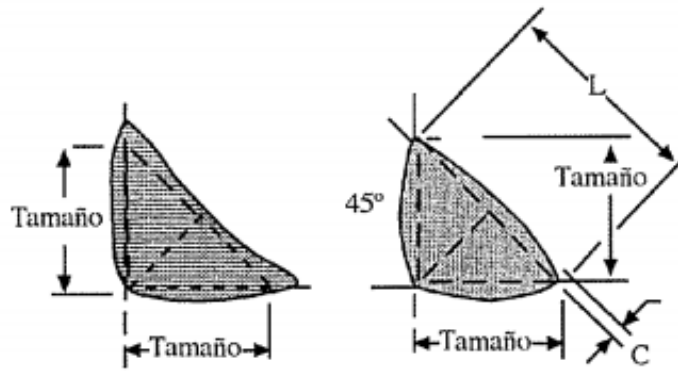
87 Perfil aceptable de soldadura de filete.
